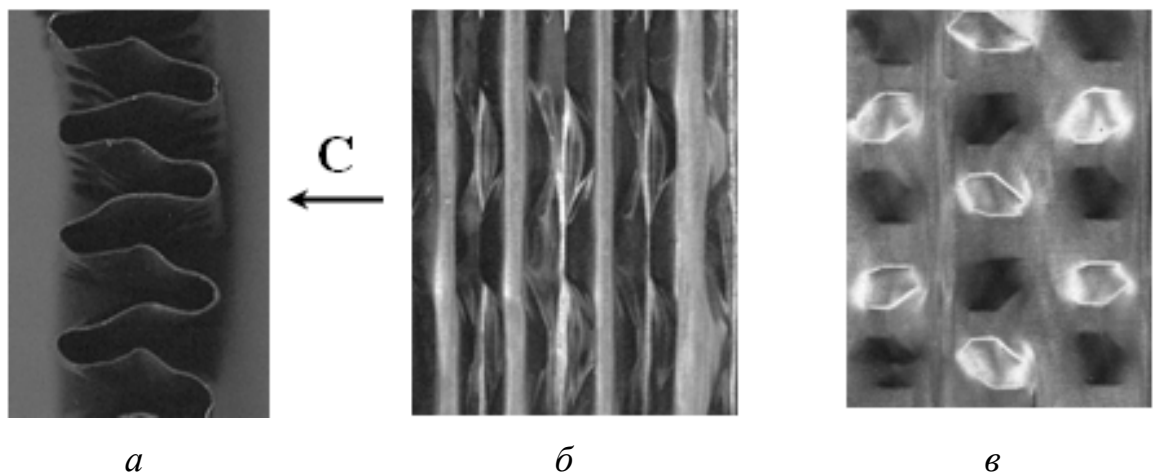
Фото елементів ребра (штамповано-гофрованої стрічки): а – вид з боку фронту; б – вид з боку гофрів (за стрілкою С); в – розгортка стрічки
